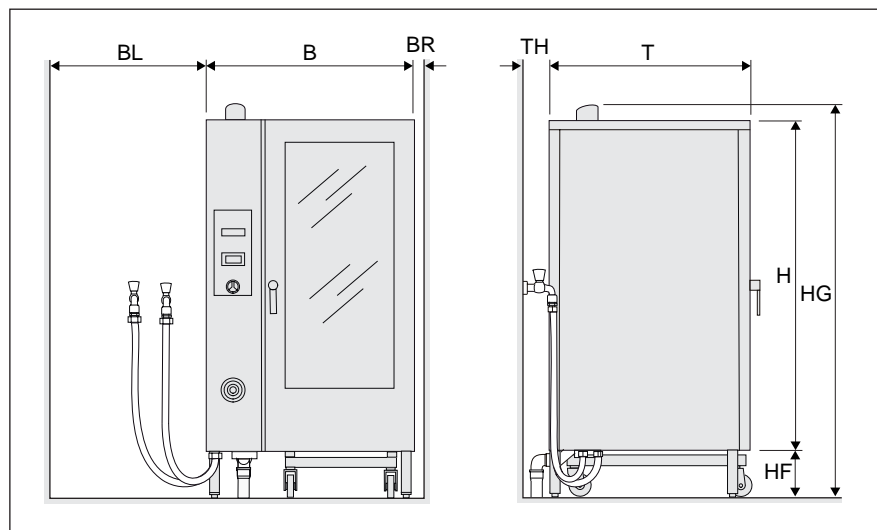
Dimensões de instalação do vaporizador combinado 215/220
